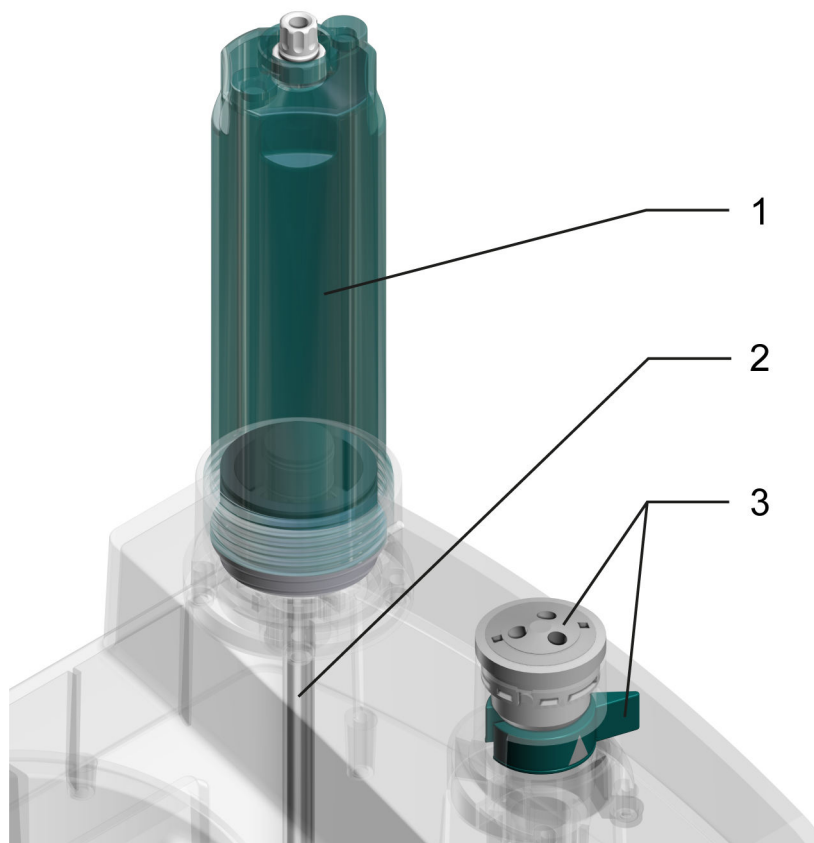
Unidad de cilindro y motor de dosificador – Visión conjunta
